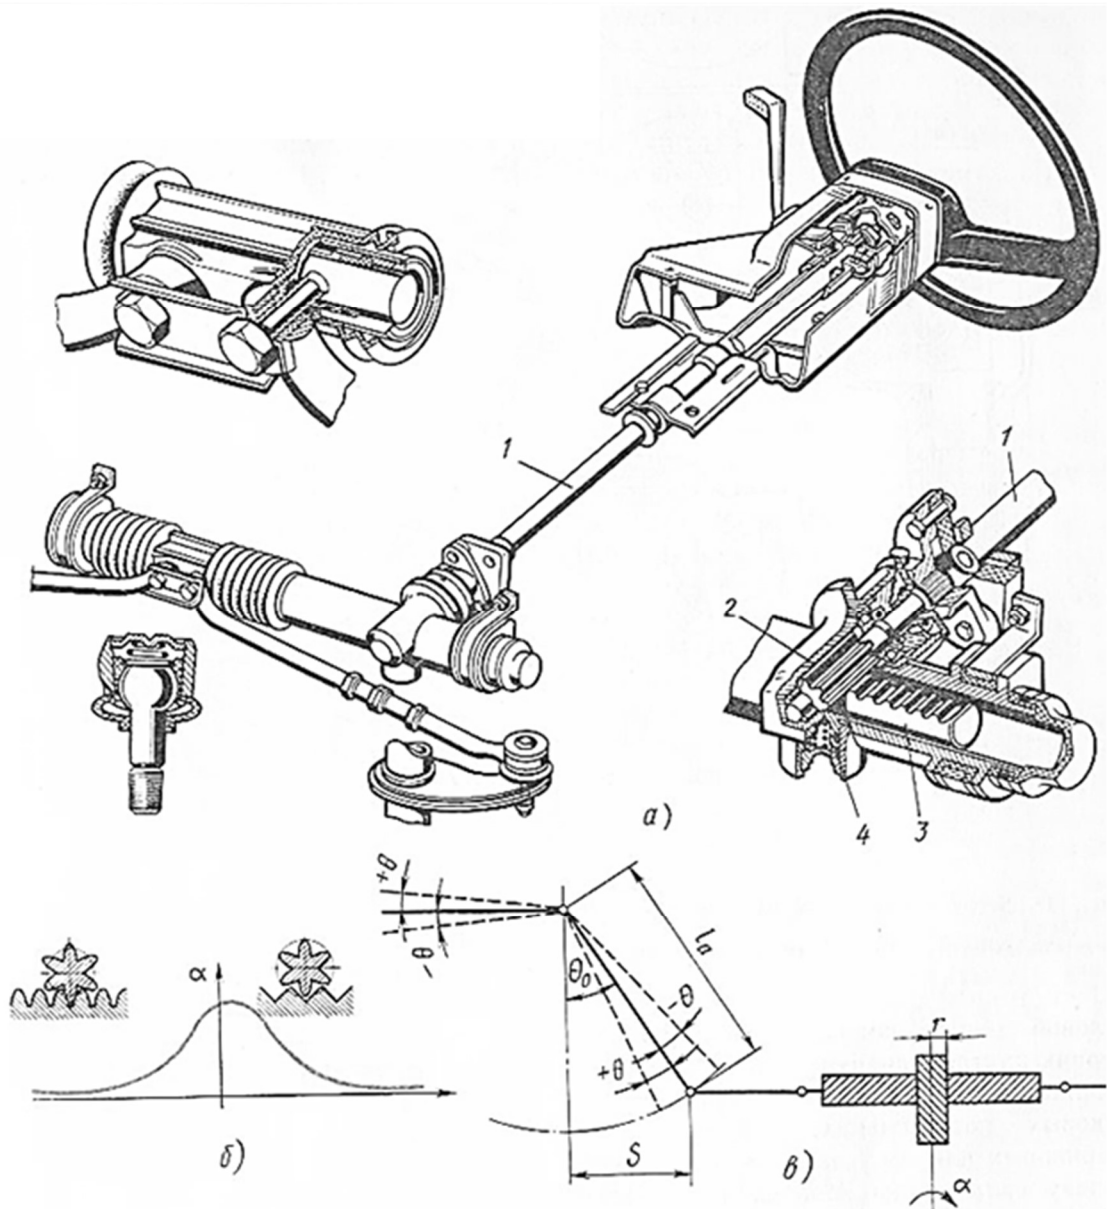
Реечный рулевой механизм: *а* – конструкция; *б* – характеристика переменного передаточного числа; *в* – схема для определения передаточного числа рулевого управления; 1 – рулевой вал; 2 – шестерня; 3 – рейка; 4 – упор
